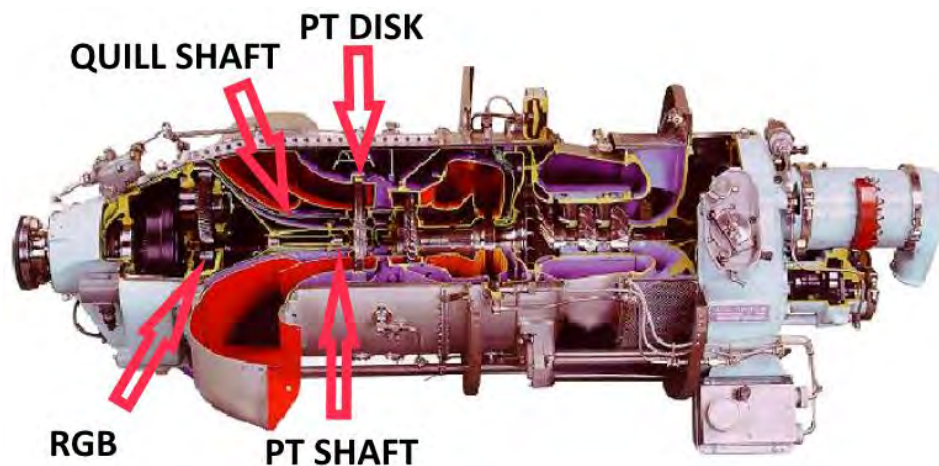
motore M601 D con evidenziati dalle frecce il *PT shaft* ed il *quill shaft* all'interno del *supporting cone*, tra *power turbine* e *reduction gearbox*.
